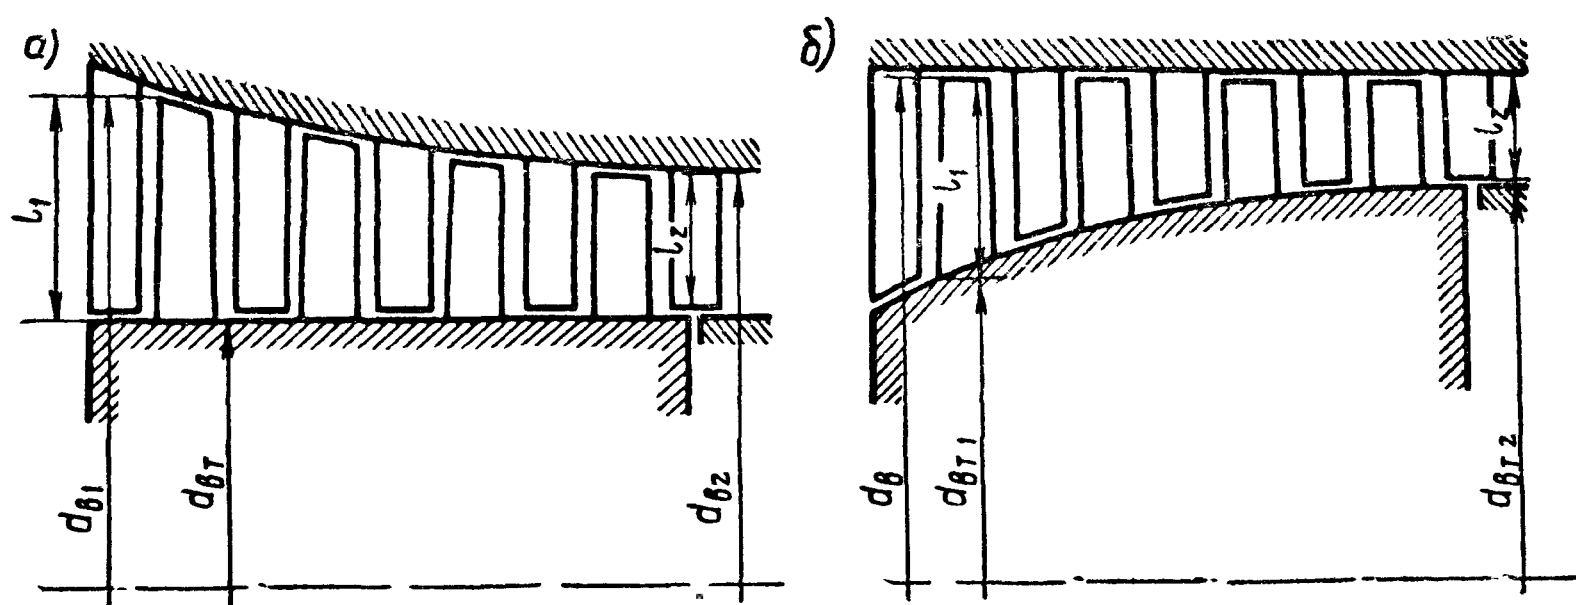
Основные схемы выполнения проточной части осевых компрессоров
